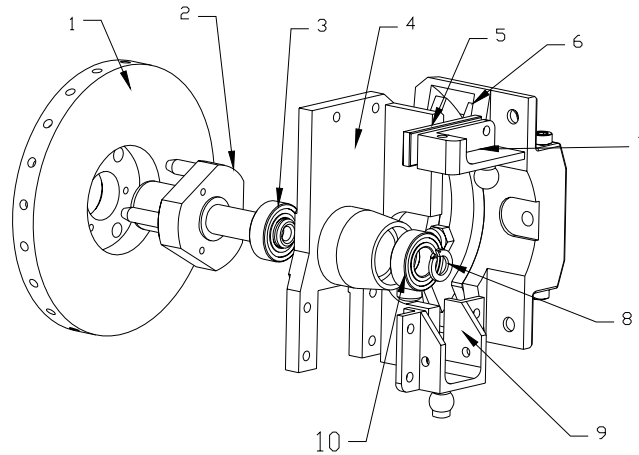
Caixa davantera. 1.Conjunt disc fre. 2.Eix. 3.Rodament boles. 4.Boixa. 5.Ajustament camber. 6. Conjunt pinça fre. 7.Anclatge triangle superior i barra direcció. 8.Anell elàstic. 9.Anclatge triangle inferior i push-rod. 10.Rodament boles.
